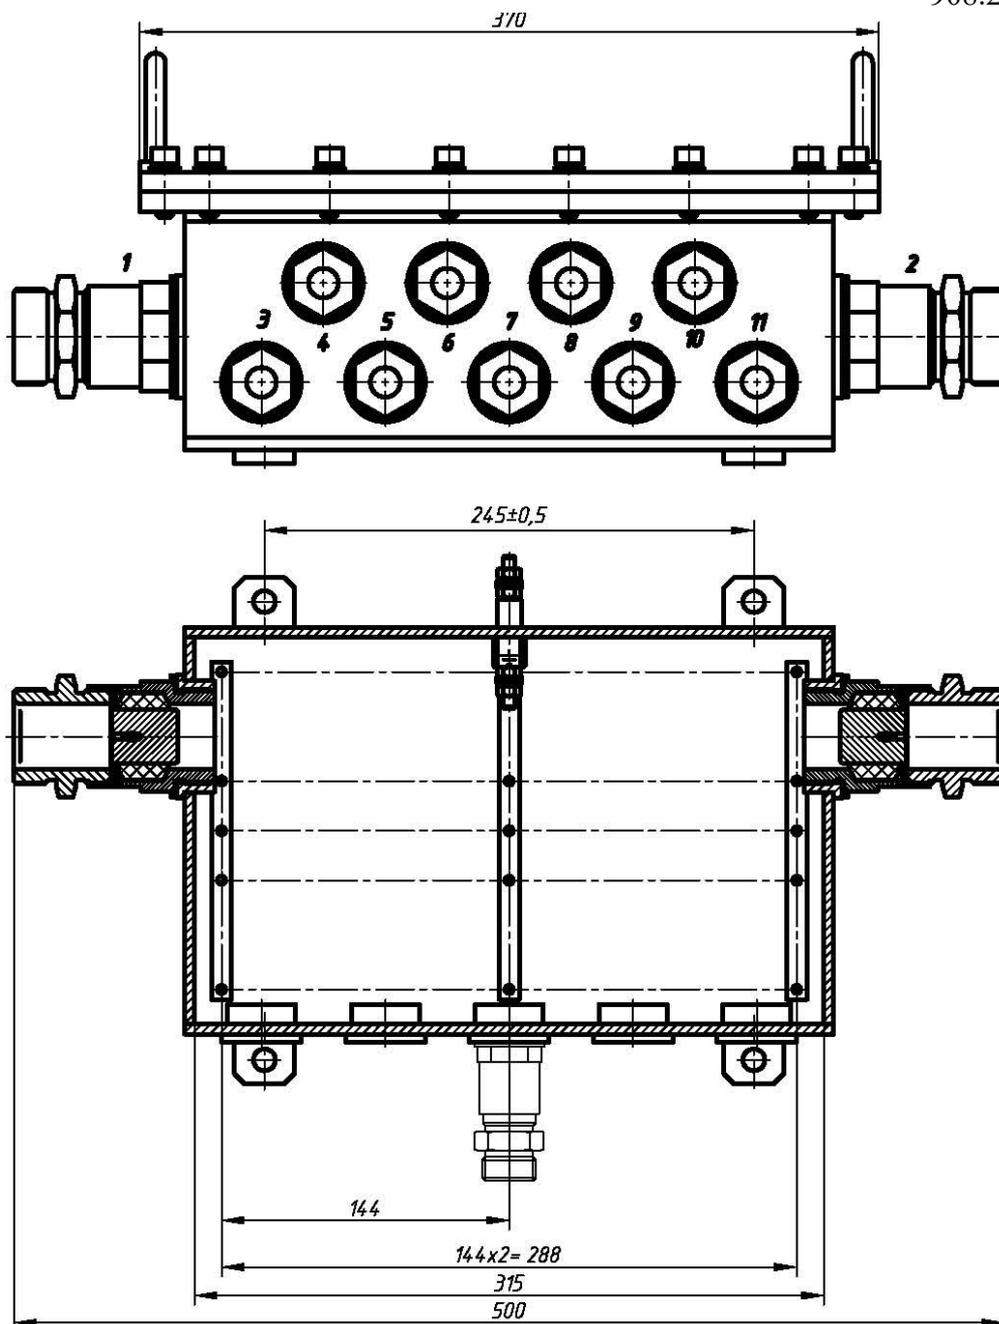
Габаритные, установочные и присоединительные размеры базовой коробки ЕхКСУВ-ПС370. Остальное см.отреть рисунок В.1.
